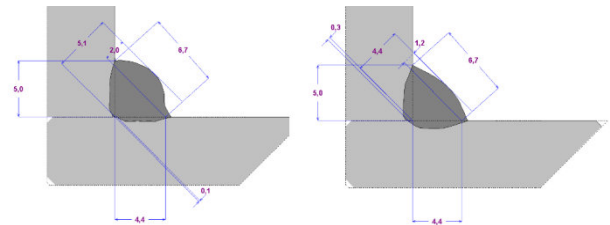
Mit SimWeld berechnete Nahtgeometrie einer Kehlnaht bei unterschiedlichen Schweißparametern
